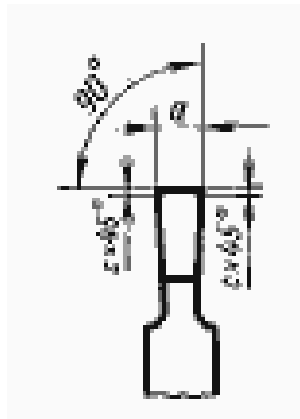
Заточка резца для обработки канавки
